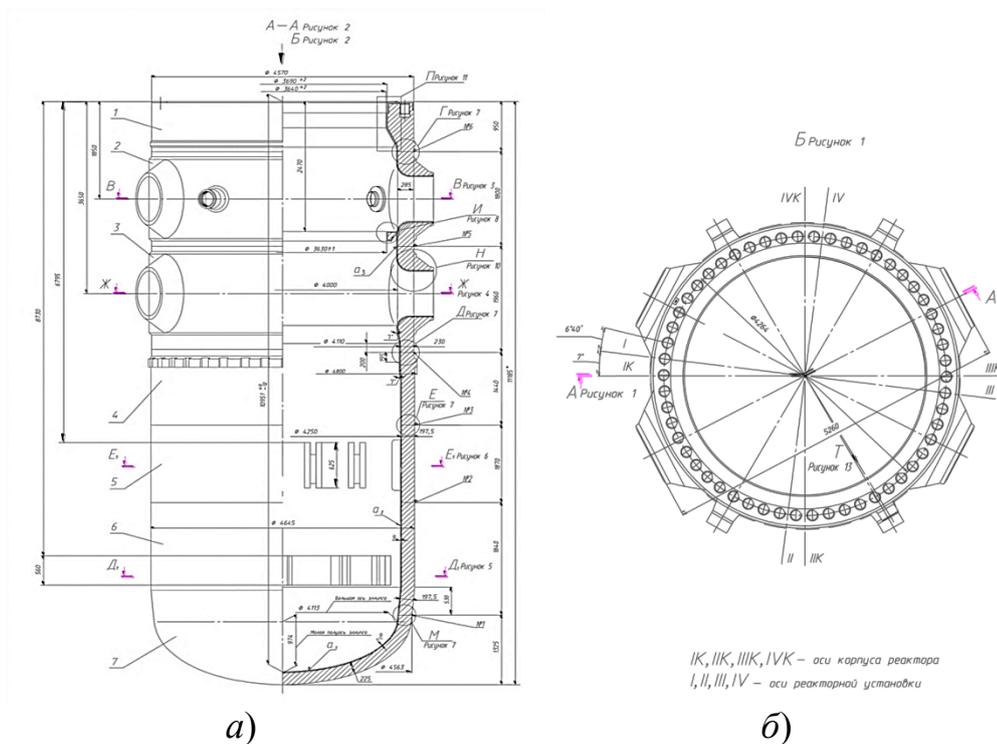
Корпус реактора ВВЭР-1200: а – вид сбоку, б – вид сверху
